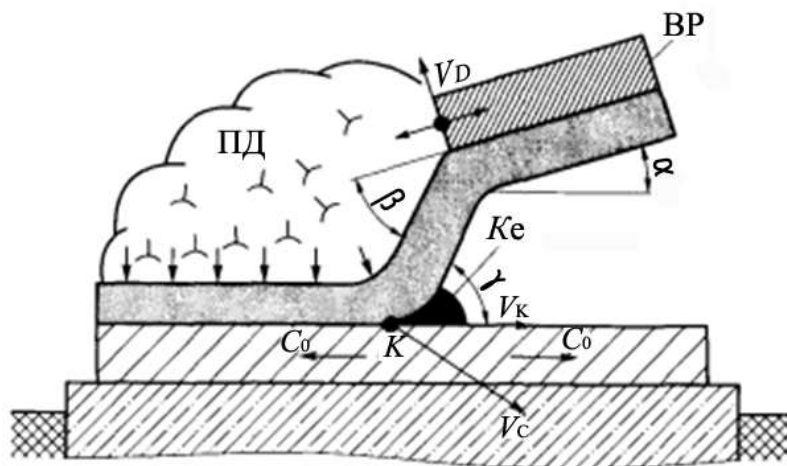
Схема співудару пластин при зварюванні вибухом:
